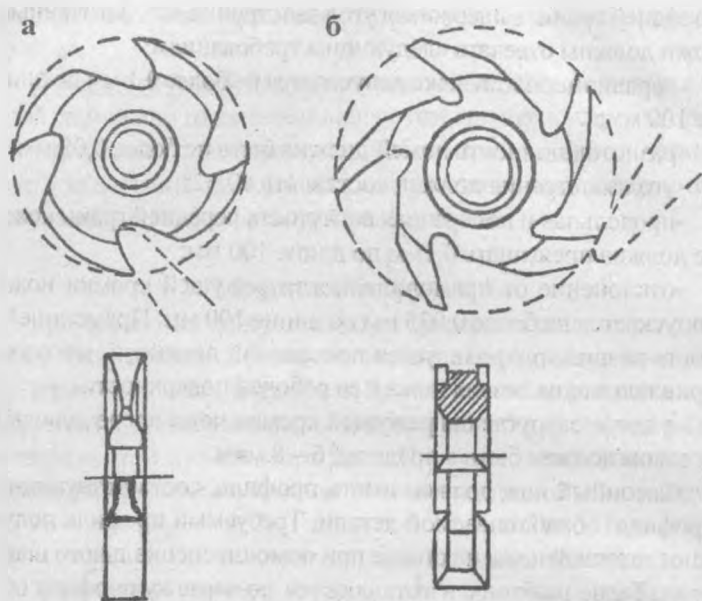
Насадные цельные фрезы к четырехстороннему продольно-фрезерному станку:
